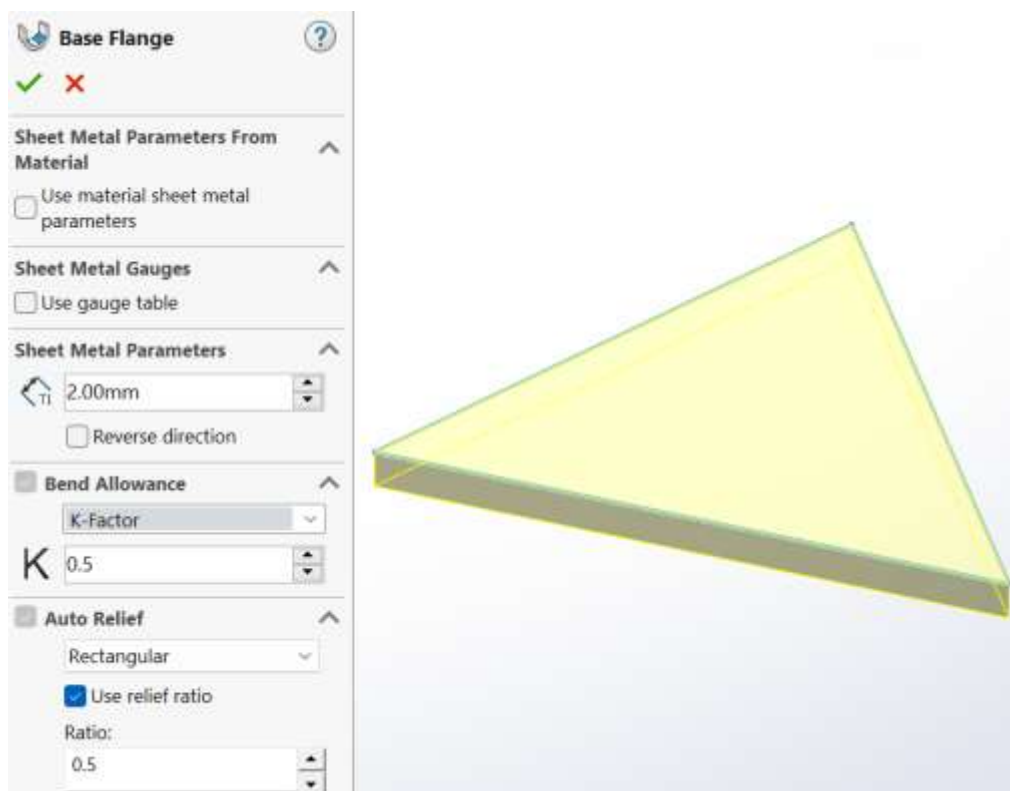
Налаштування побудови деталі з листового металу
